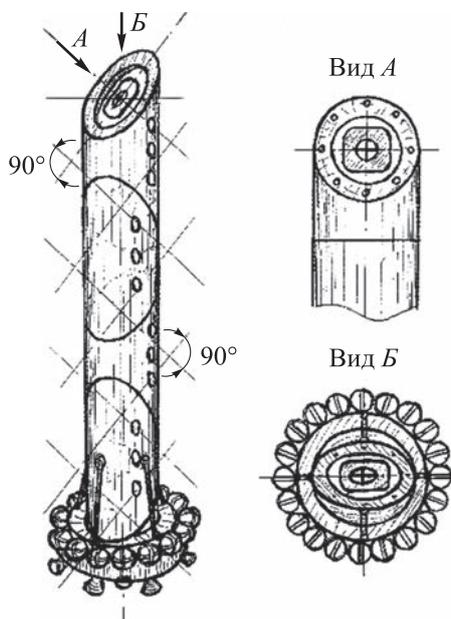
Сборка из четырех УСКМ с формообразующей поверхностью эллиптического цилиндра
